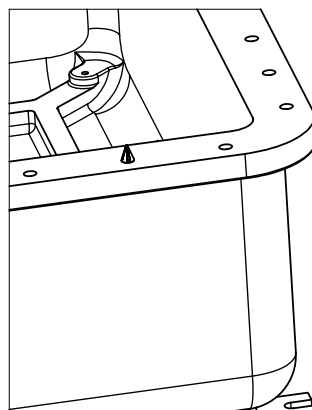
Проверка контактной поверхности на корпусах ЩОРВ, ССFE, AQS, МКВ-S13, КСВ, ШМВЗ, ШЭКВ
